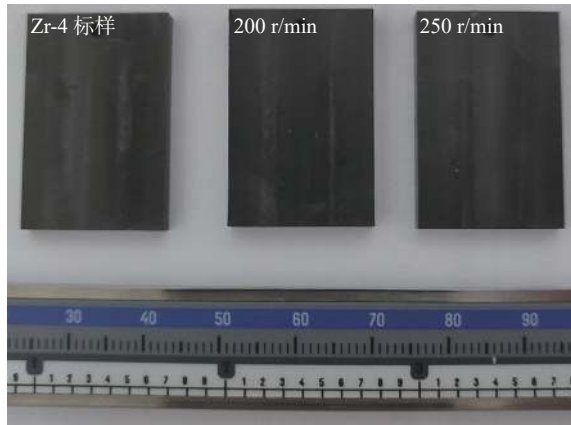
母材和 FSW 接头腐蚀后的宏观形貌
